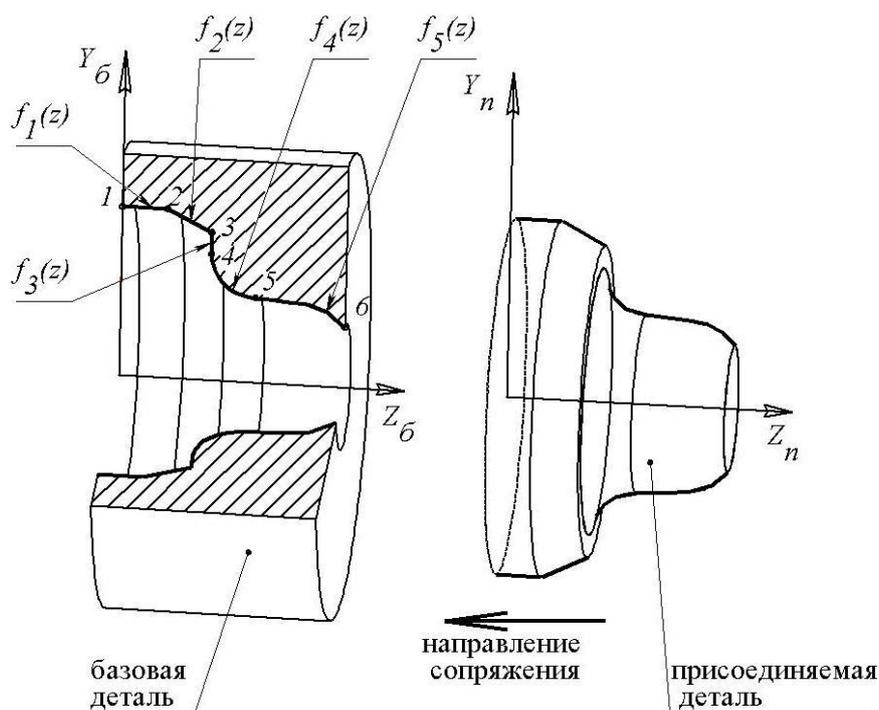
Пример формы образующей сопрягаемой поверхности базовой детали, которая обеспечивает возможность сопряжения по ней присоединяемой детали только с переустановкой базовой детали в шпинделе станка
